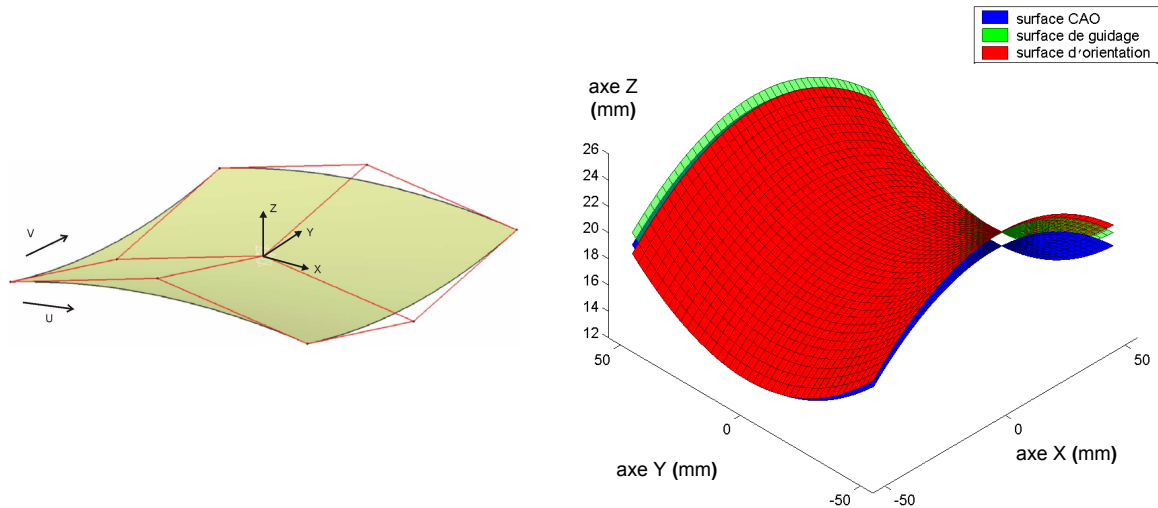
Géométrie du carreau et modèle de surface d'usinage
